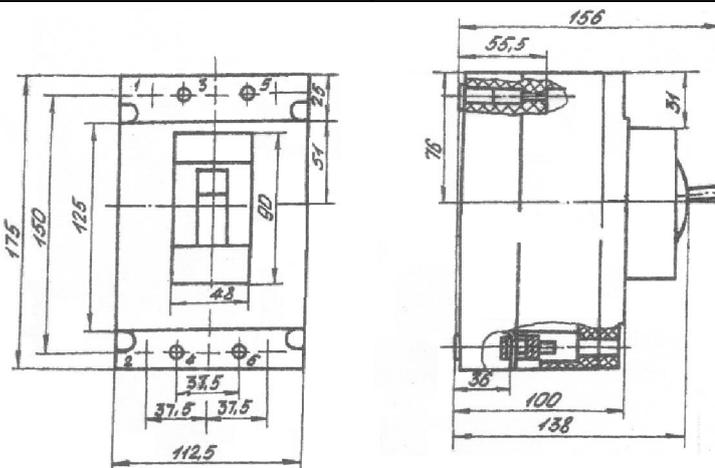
Габаритные размеры выключателя ВА-5935
